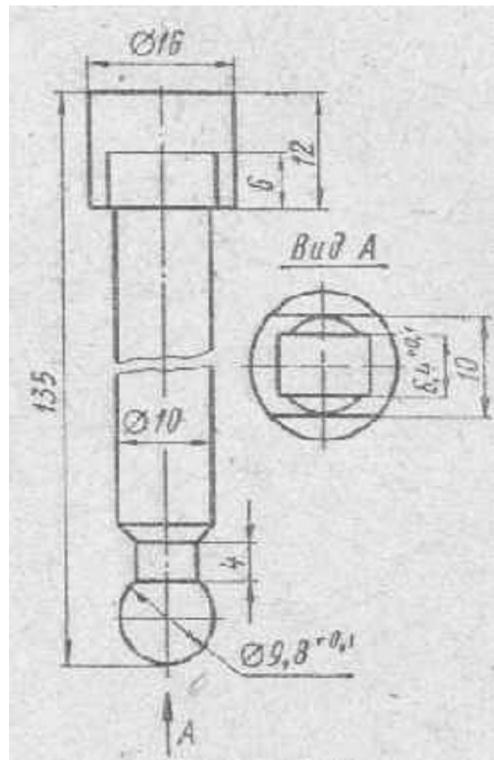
Стержень к универсальному приспособлению для выпрессовки подшипника
